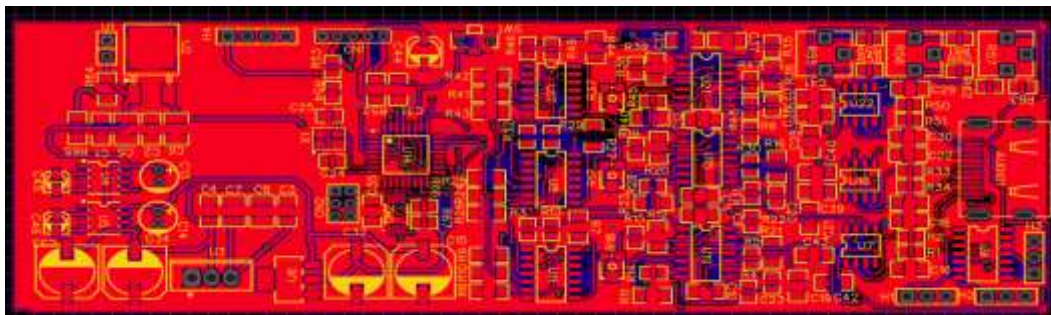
Probe μέτρησης. Σχέδιο πλακέτας pcb.
